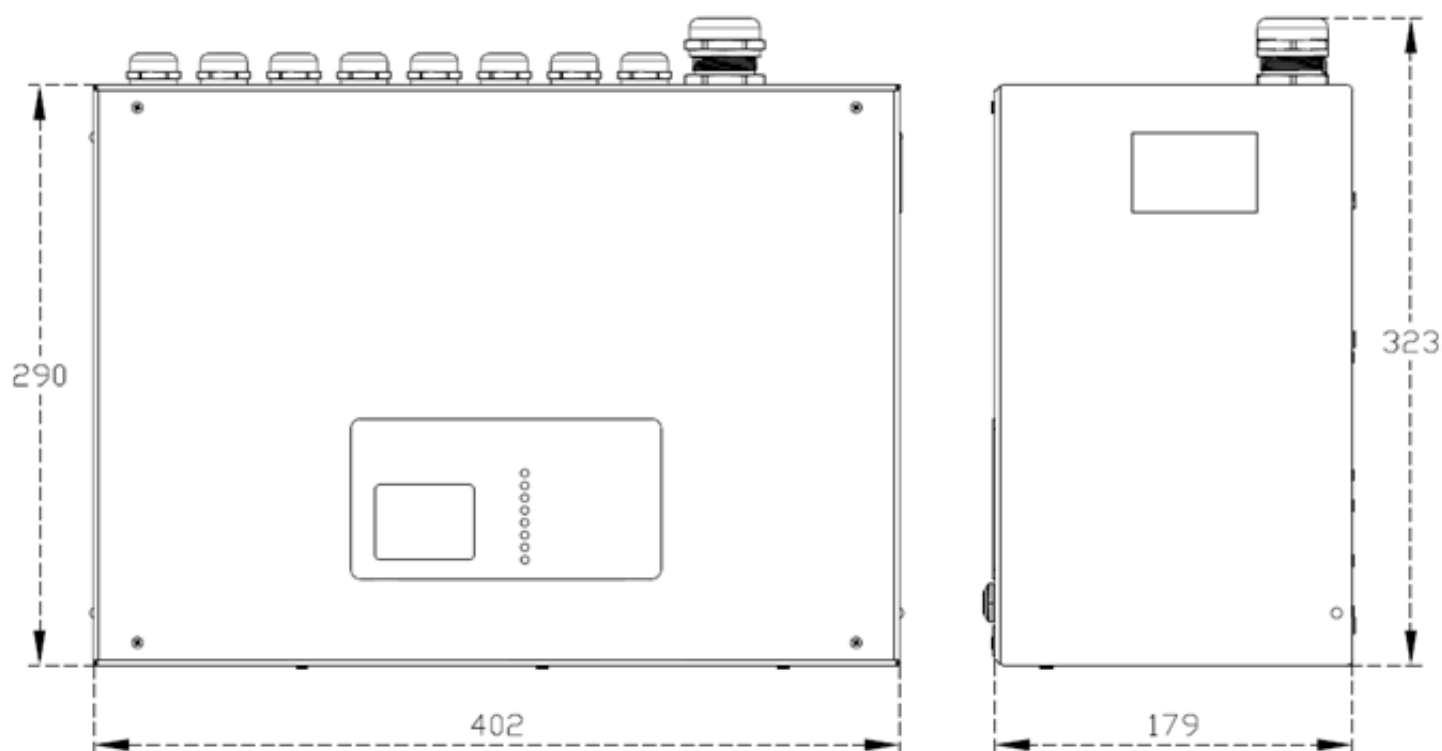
Габаритные размеры и внешний вид прибора NRD-02 2201AC
